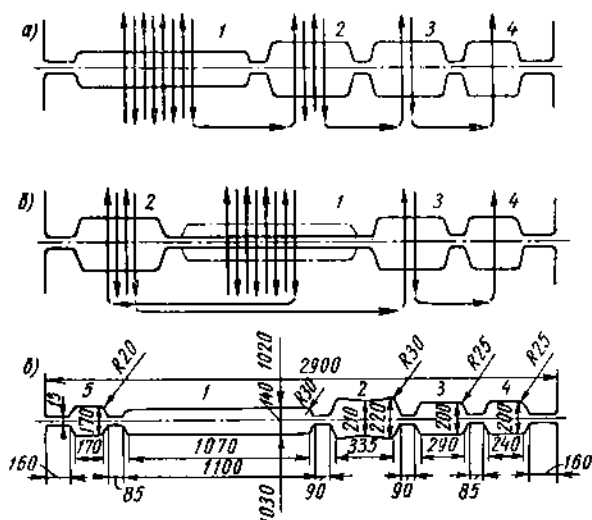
Схема прокатки и размещения калибров в блюмингах
